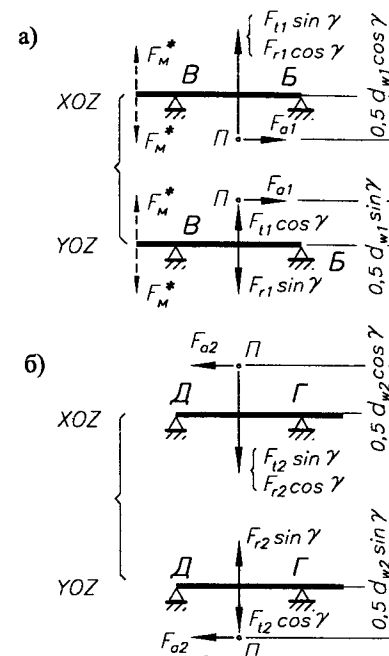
Расчетные схемы: а) вала 1; б) вала 2
